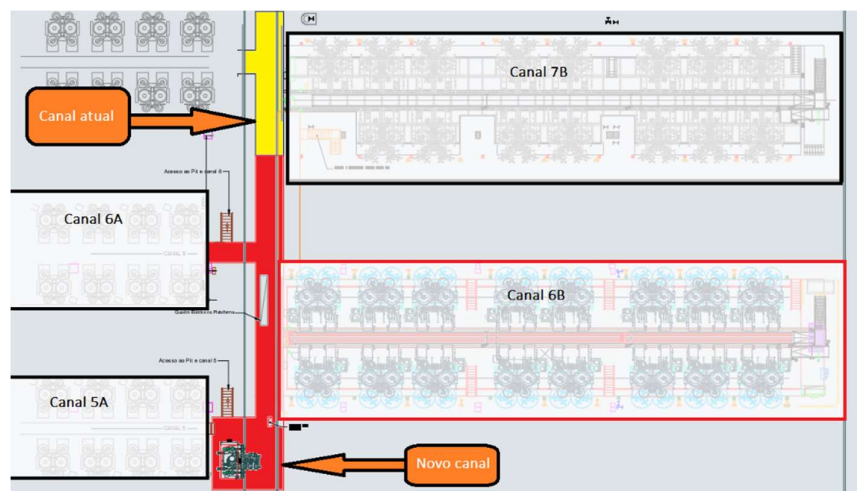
Esquematização da planta dos canais circundantes ao canal 6B
